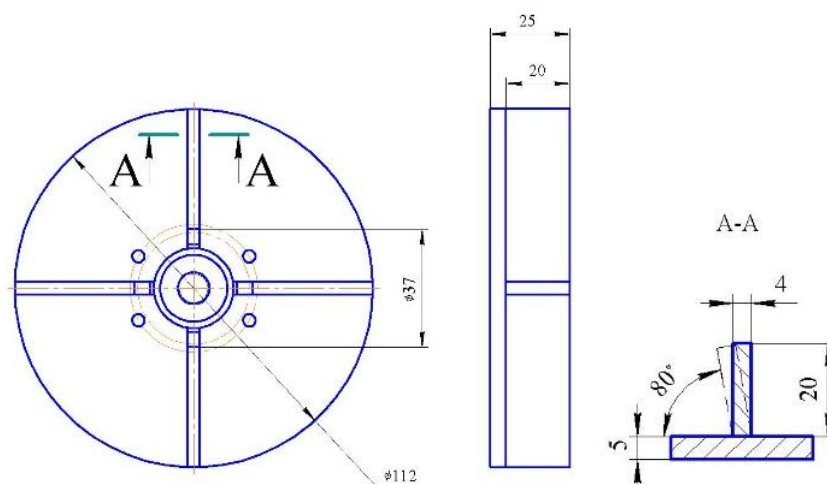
Схема рабочего колеса с 4-мя прямыми лопастями
